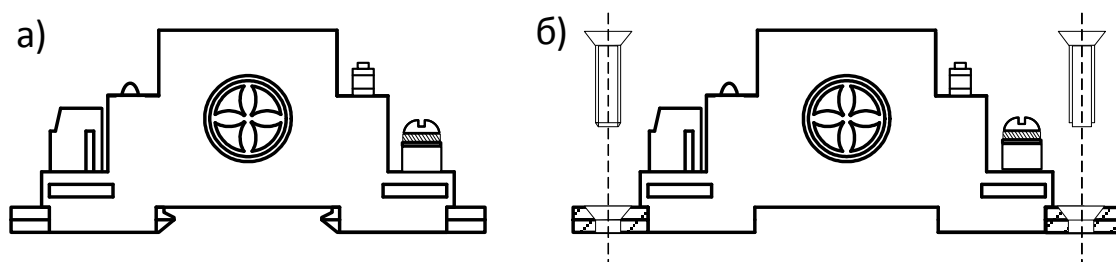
Способы крепления устройств Commeng Compact OVP (а-на рейку DIN, б-к поверхности).
